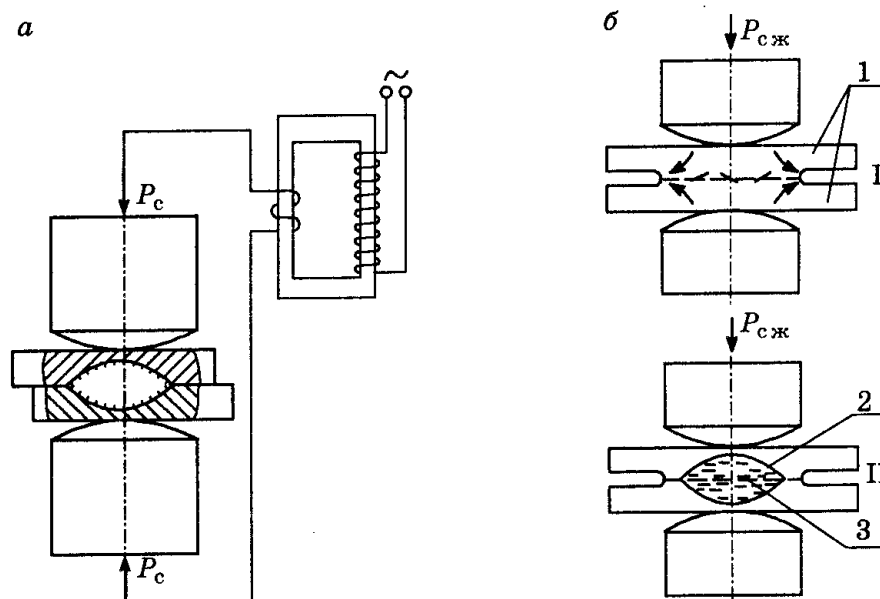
Схемы процесса (а) и образования сварного соединения (б) при точечной контактной сварке: 1 — начало; II — конец
